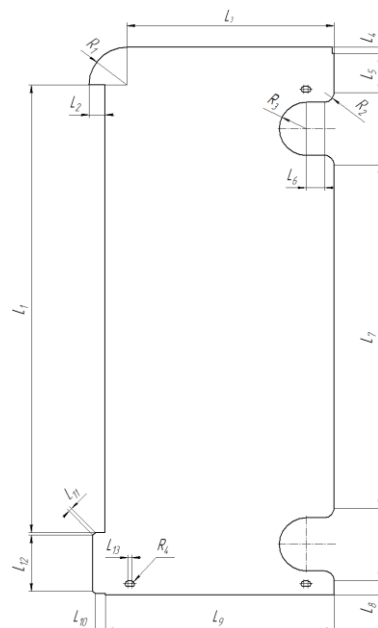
Схема розмірів контуру деталі «стінка»
